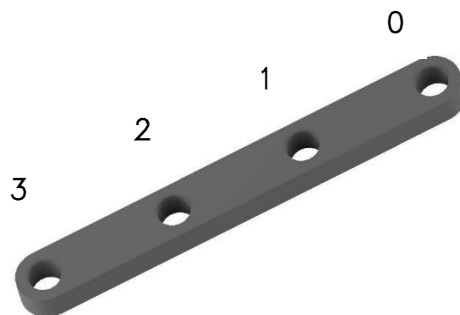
Uniray-Fly-Pro-Serie-Lastadapter hinten mit vier Bohrungen 8 mm
